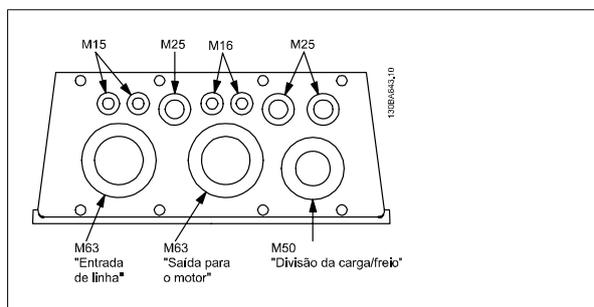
Furos para entrada do cabo do gabinete metálico C1. As sugestões de uso dos furos compreendem apenas recomendações; outras soluções são possíveis.
